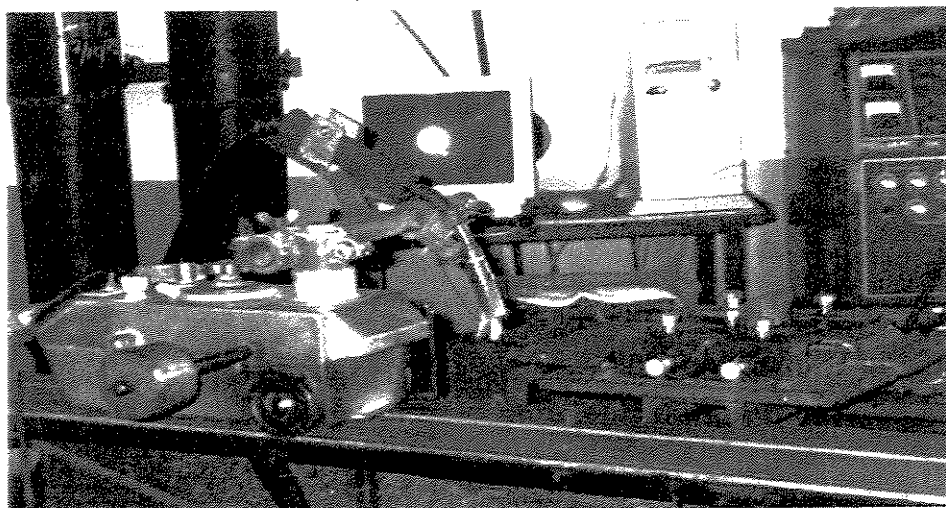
Montagem para semi-automatização do processo de soldagem
